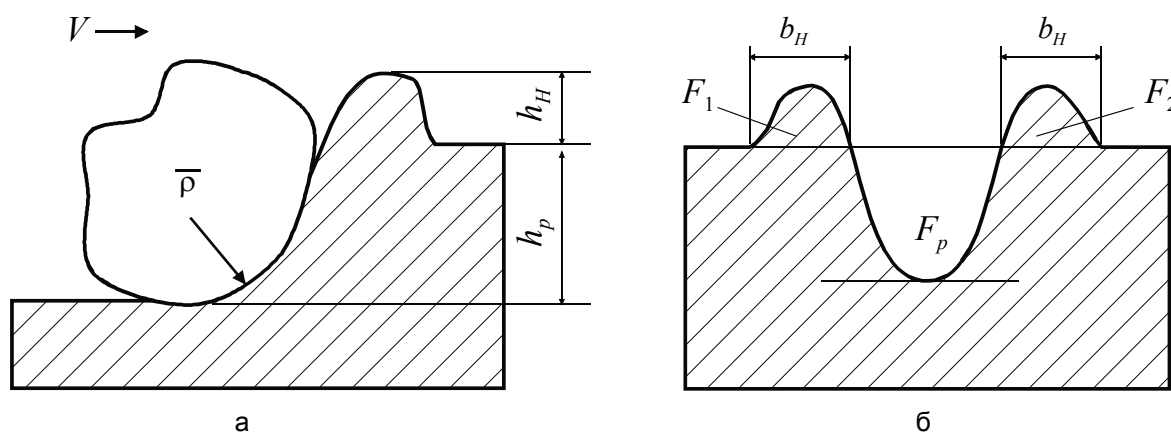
Взаимодействие абразивного зерна и обрабатываемого металла при шлифовании металла:
